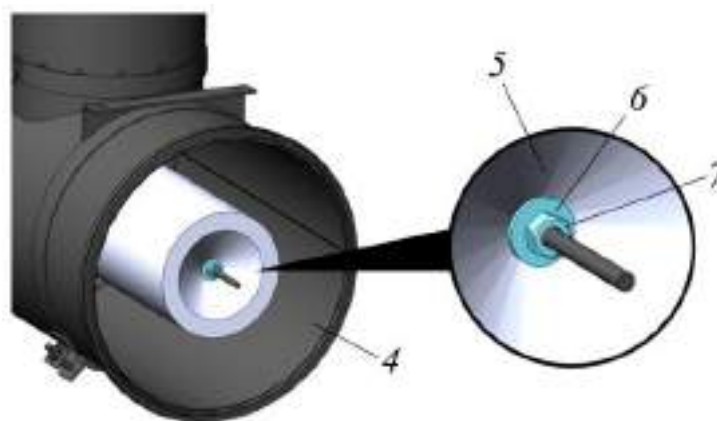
Процедура извлечения из корпуса дополнительного фильтра
